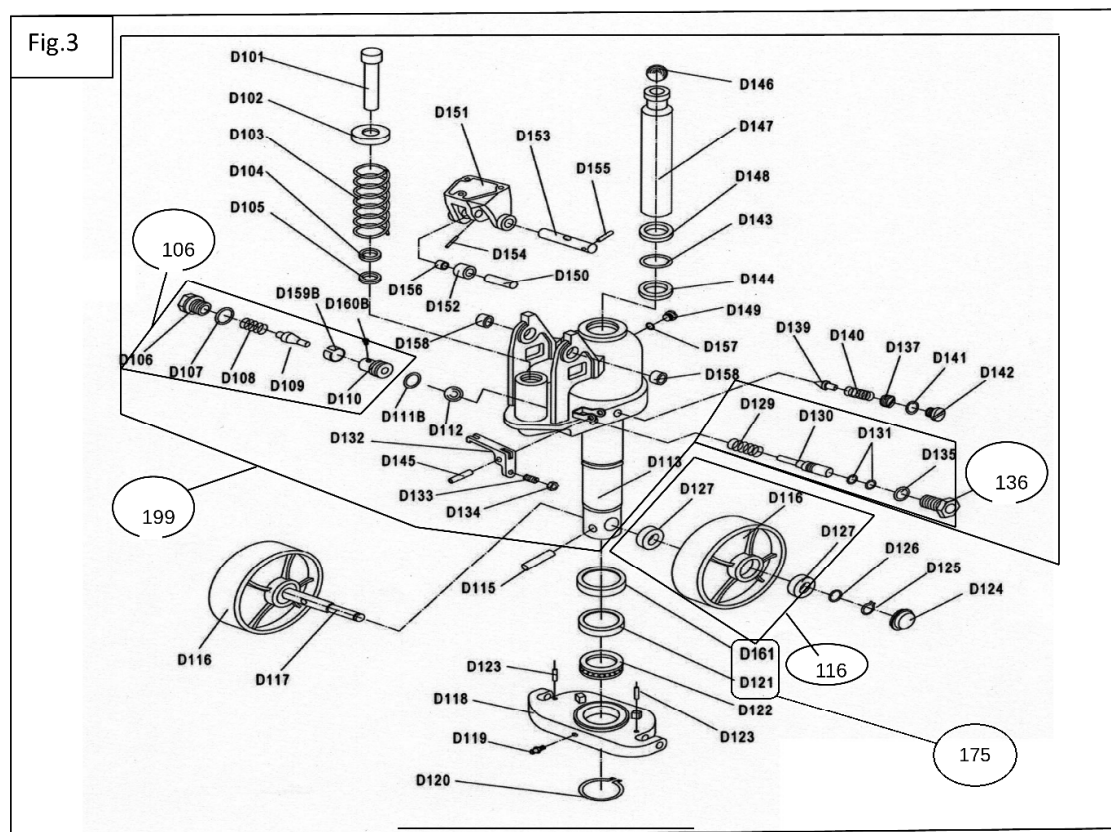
Despiece: conjunto hidráulico y ruedas
